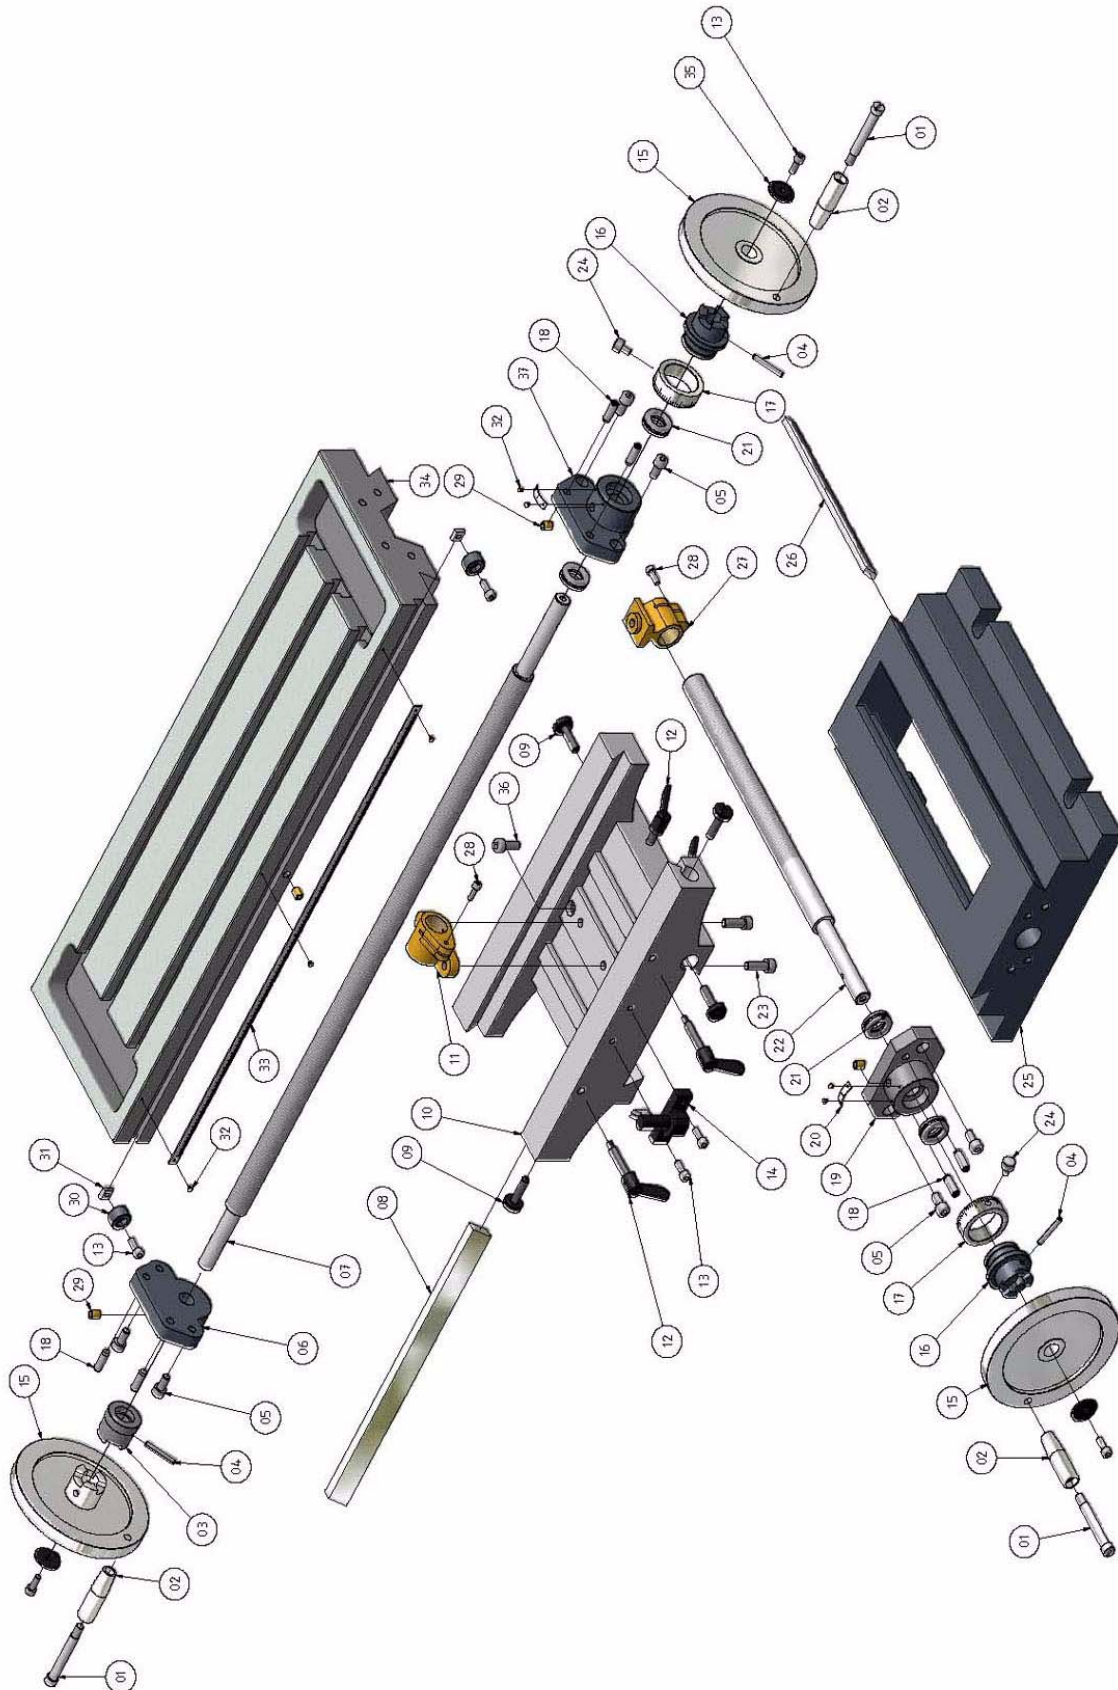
Ersatzteilzeichnung - Drawing spare parts
